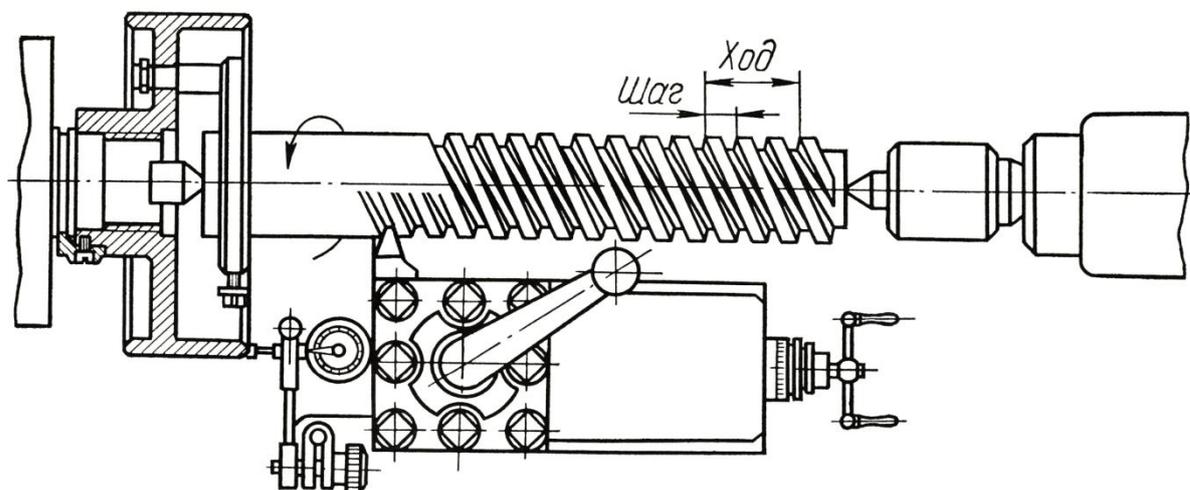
Перемещение суппорта на шаг резьбы с отчётом по индикатору
